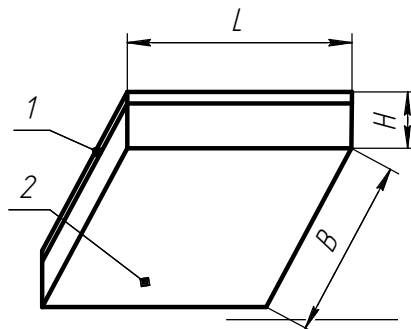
ЛПО46-4х18; 1. Корпус в сборе, 2. Рассеиватель
